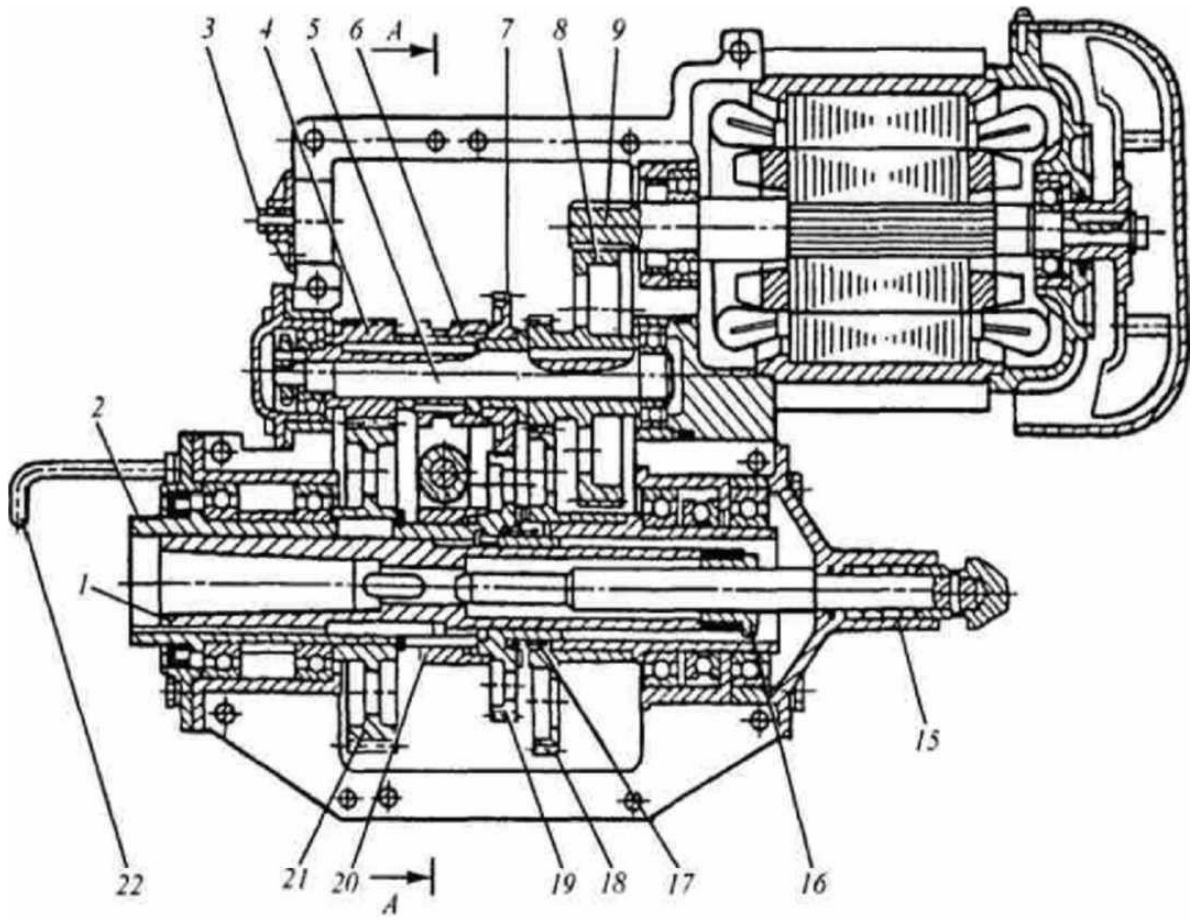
Мотор-редуктор рельсосверлильного станка РСМ 1М
